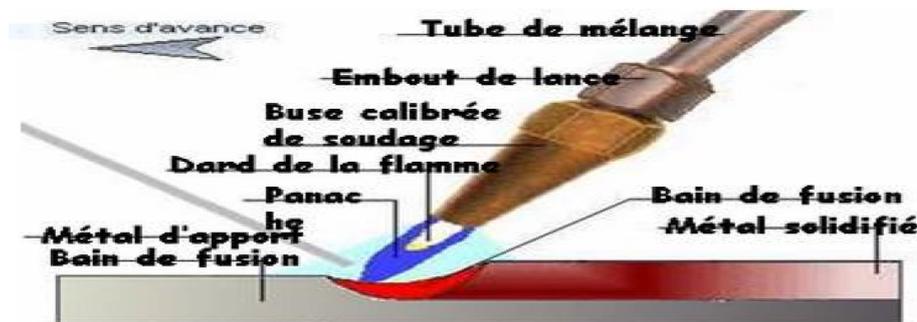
soudage Oxyacétylénique.
